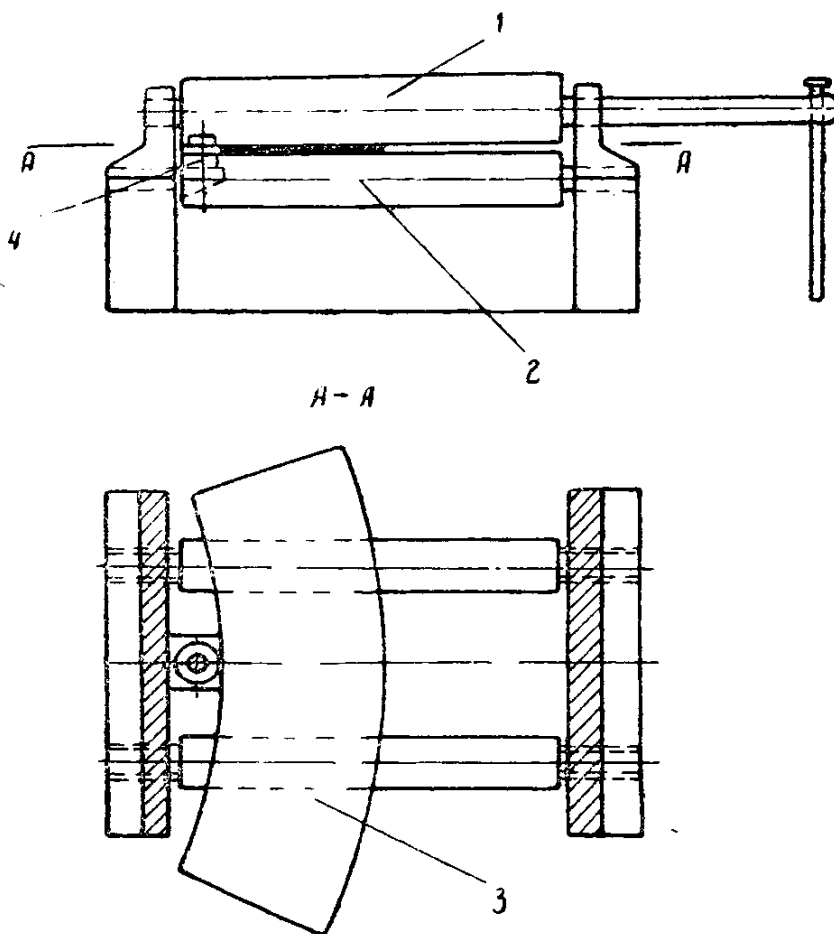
Кронштейн с коническим роликом: 1 — верхний валок; 2 — нижний валок; 3 — заготовка; 4 — ролик.
